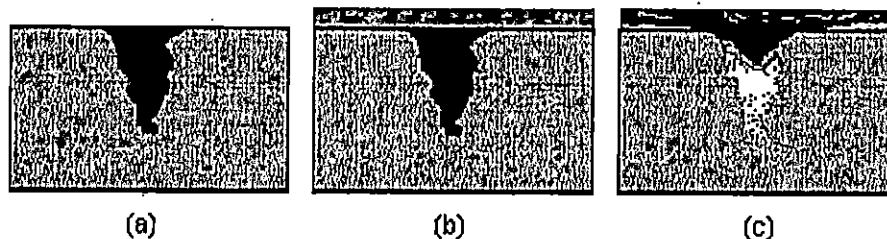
Aplicación de un líquido penetrante sobre una junta de soldadura, para detectar defectos no apreciables a simple vista ni a pruebas de VT ⁽¹⁻³⁶⁾
